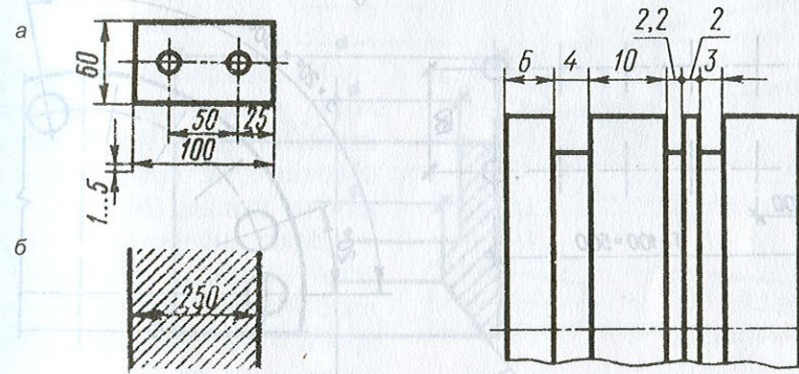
Нанесение размеров на чертежах: а — размерная стрелка, б — размер на заштрихованной площади чертежа
